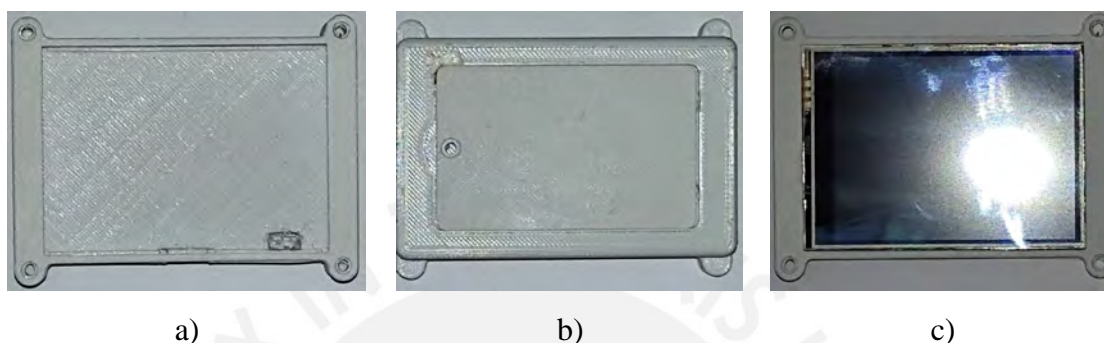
Caja electrónica fabricada: a) vista superior, b) vista inferior y c) encaje de pantalla
